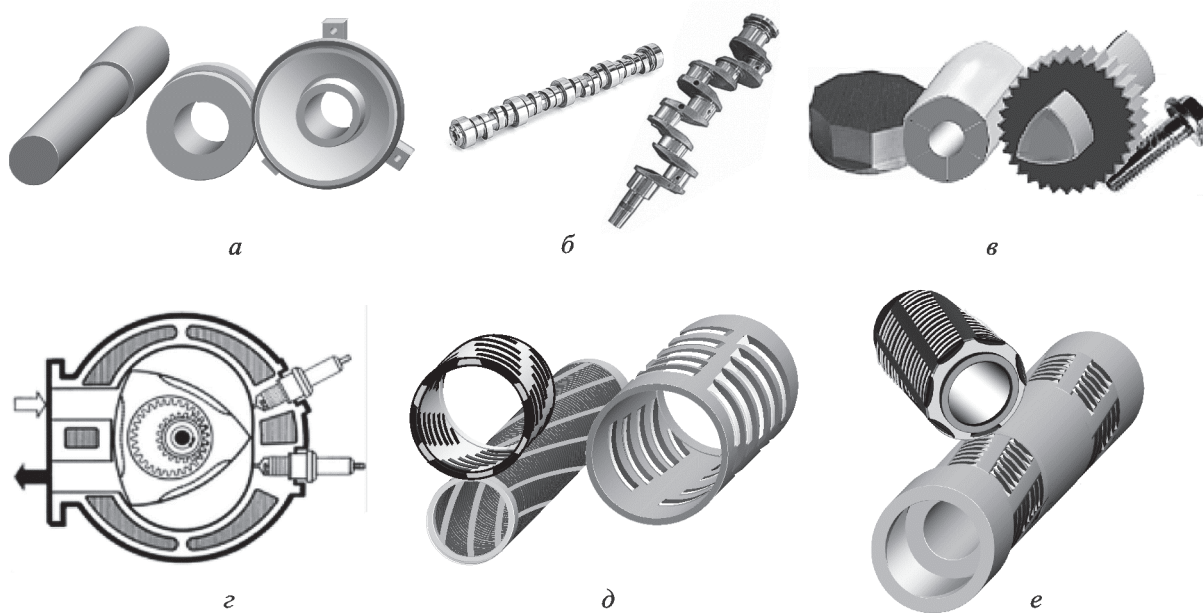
Типовые детали, получаемые многолезвийным точением и фрезерованием: *a* — гладкие валы, кольца и фланцы; *б* — профильные детали бесшпоночных соединений; *в* — распределительные и коленчатые валы; *г* — двигатель Ванкеля; *д* — щелевые фильтроэлементы и демпферы; *е* — теплообменники и оребренные детали под покрытие и смазку
